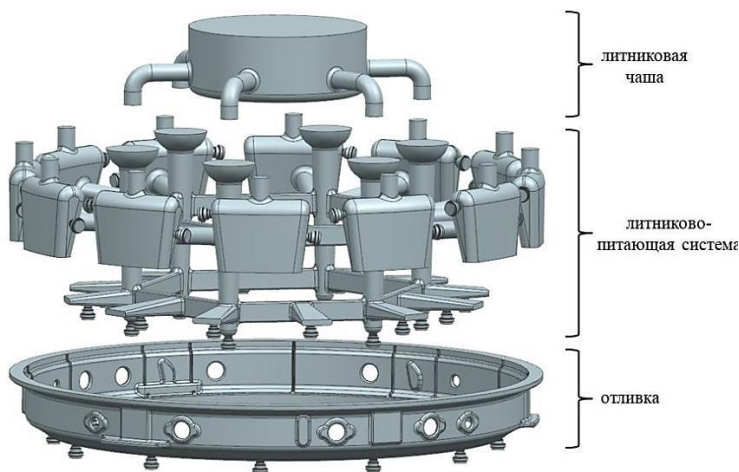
3D модель отливки детали «Корпус наружный» с литниково-питающей системой
